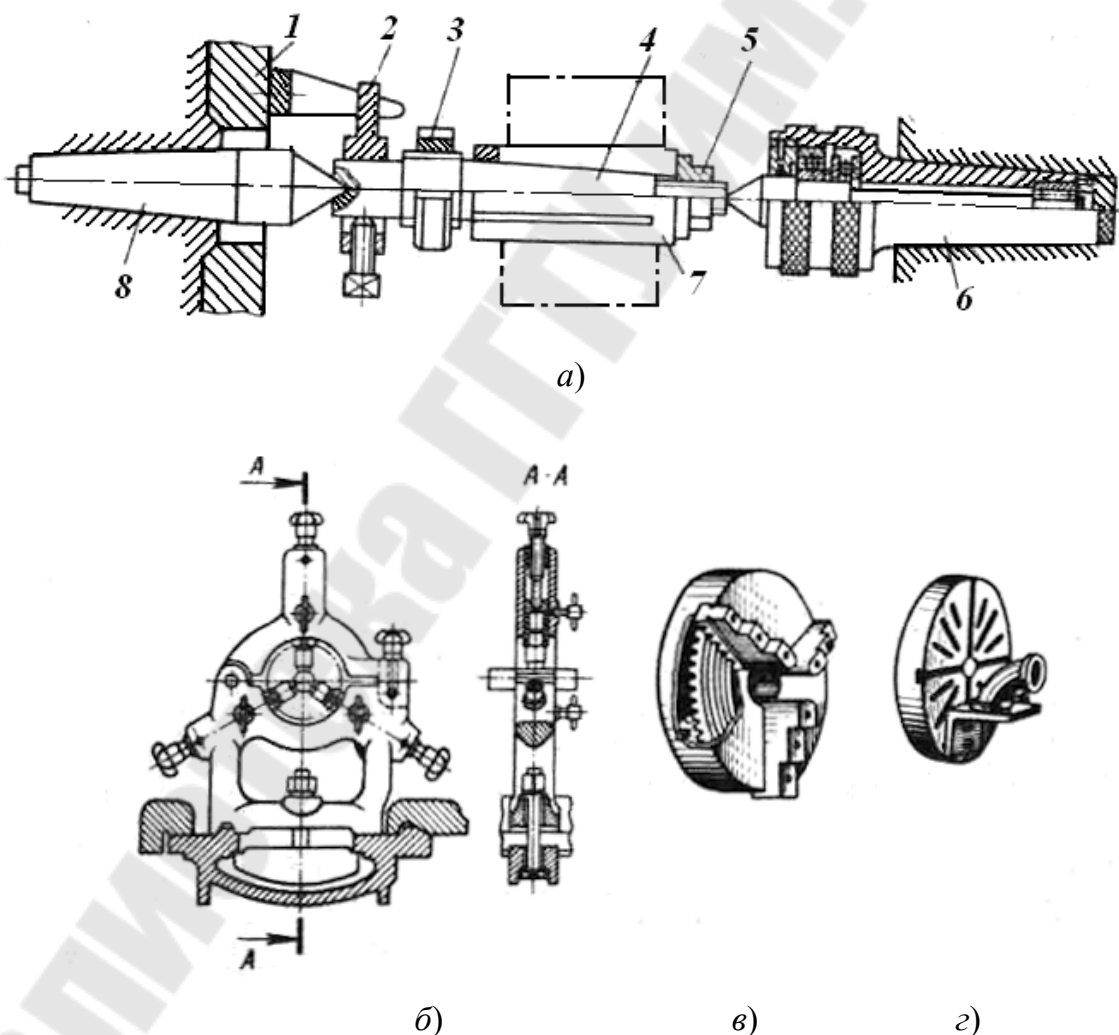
Эскизы приспособлений для установки заготовок: а – в центрах; б – в люнете; в – в патроне; г – в планшайбе
